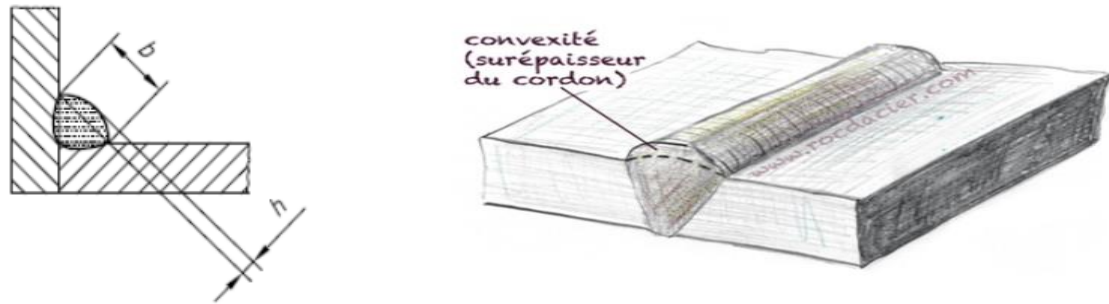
convexité dans un joint soudé (Réf.[R28])
